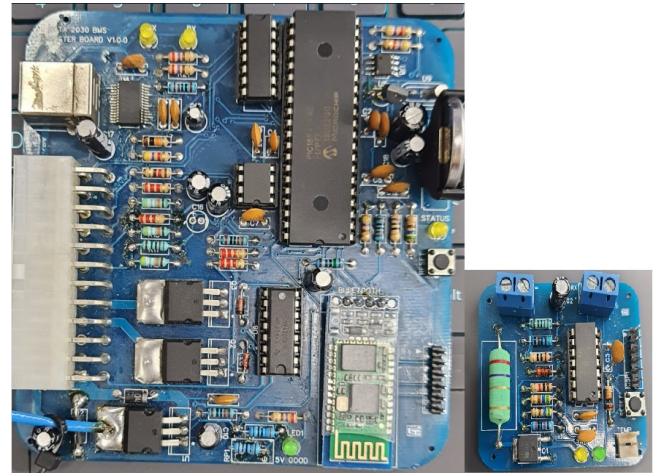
PCB *Master* (esquerda) PCB *Slave* (direita).
